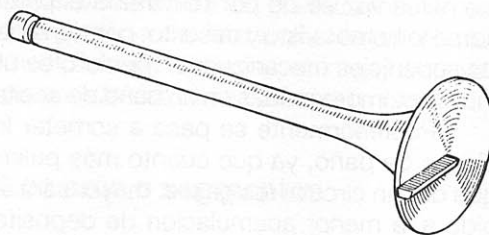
Válvula a la que se le ha soldado un trozo de acero para convertirla en una herramienta cortante.
